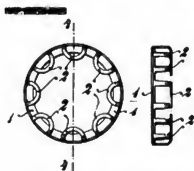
Solinger Stanwaren u. Werkzeugfabrik, Wälb, Westebbe, Solingen.
